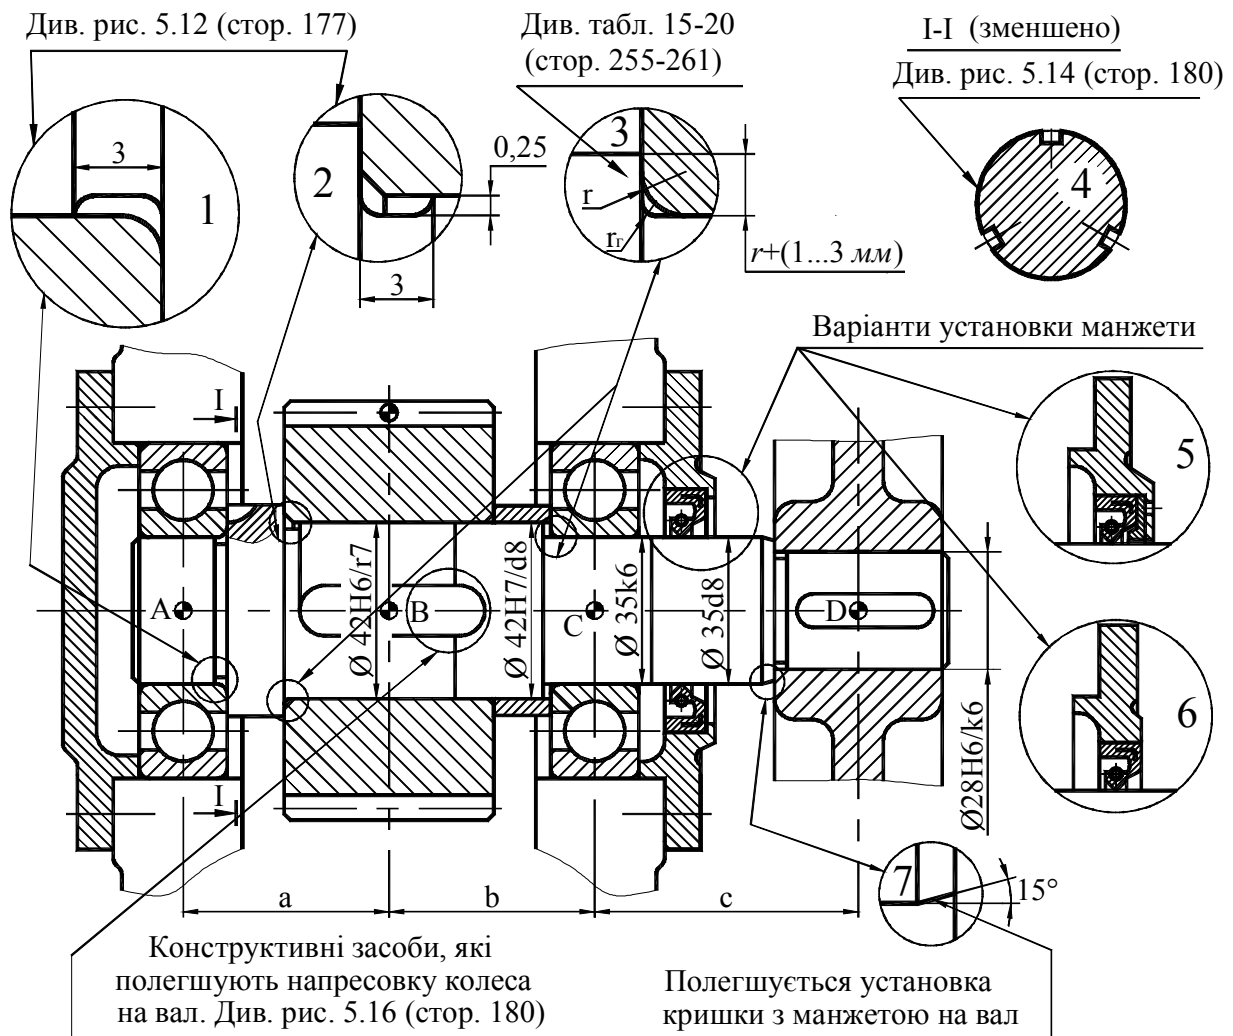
Приклад конструкції вхідного вала одноступеневого циліндричного редуктора
